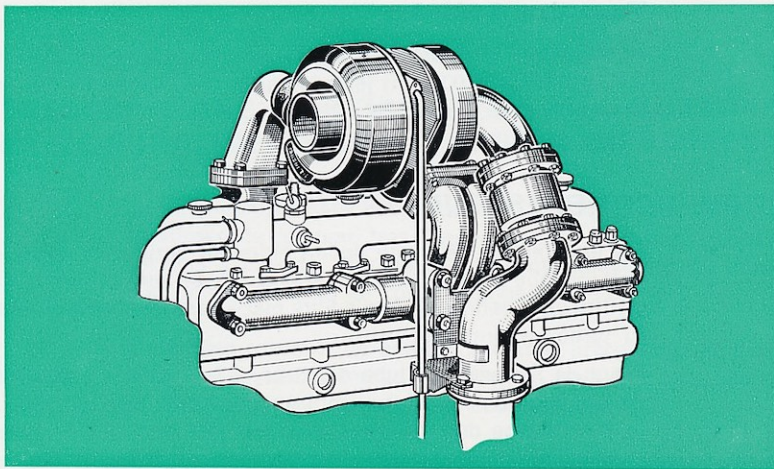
Vue d'ensemble du turbo-compresseur « HOLSET ».
